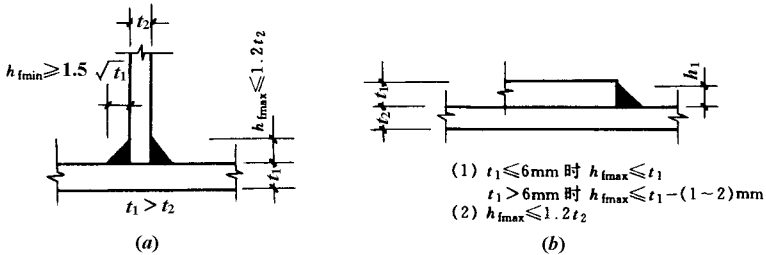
角焊缝的最大、最小焊脚尺寸
